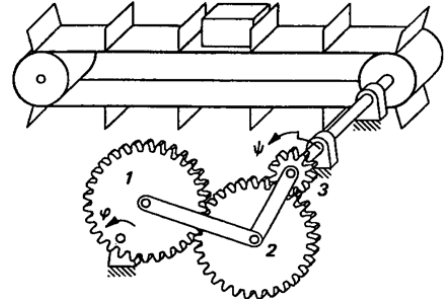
Räderkoppelschrittgetriebe in einer Verpackungsmaschine. [6].
